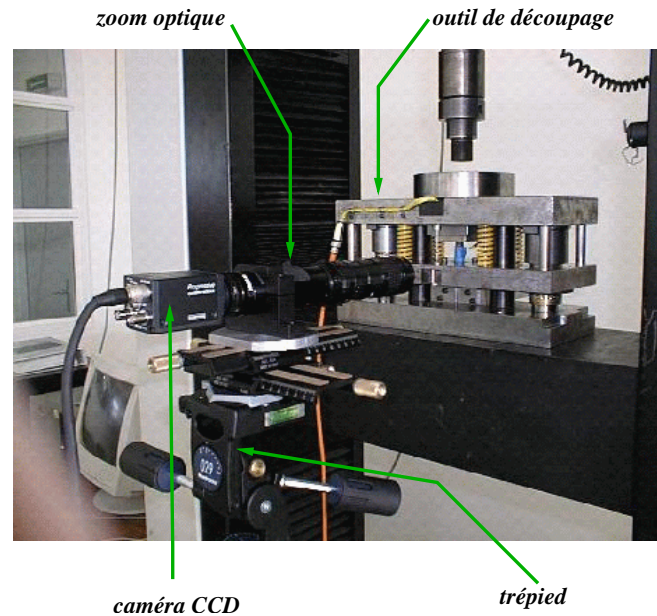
Vue d'ensemble de l'outil de découpage et du système d'acquisition vidéo.
